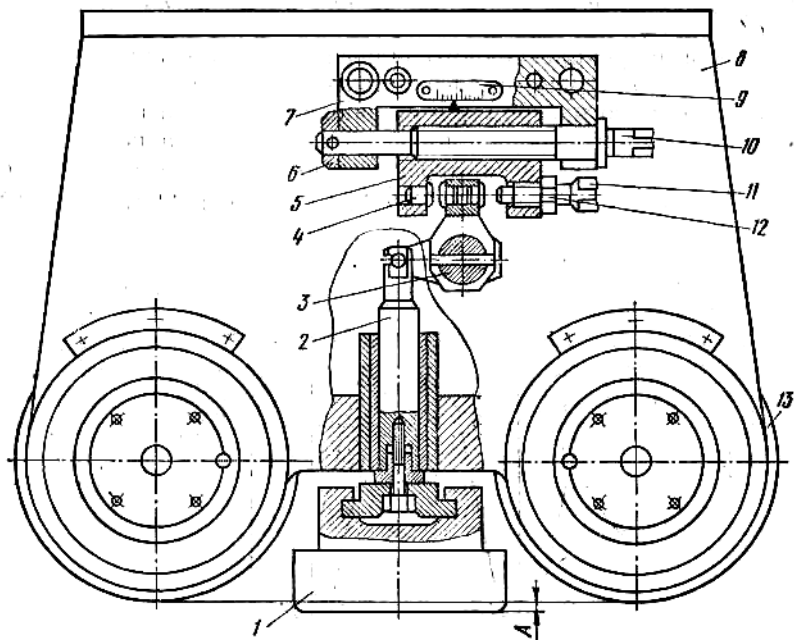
Схема механизма настройки контактной балки шлифовального станка:
